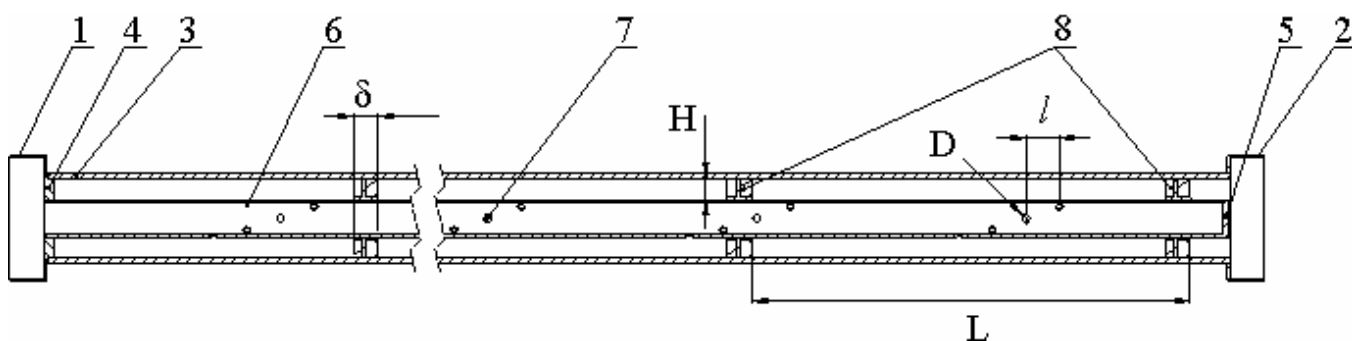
Рекуператор [84]: 1 — входящий воздушный короб; 2 — выходной воздушный короб; 3 — нагреваемая труба; 4 — входная перфорированная крышка; 5 — заглушка; 6 — внутренняя воздушная труба; 7 — отверстия-сопла; 8 — лопасти в форме винтовой крыльчатки.
